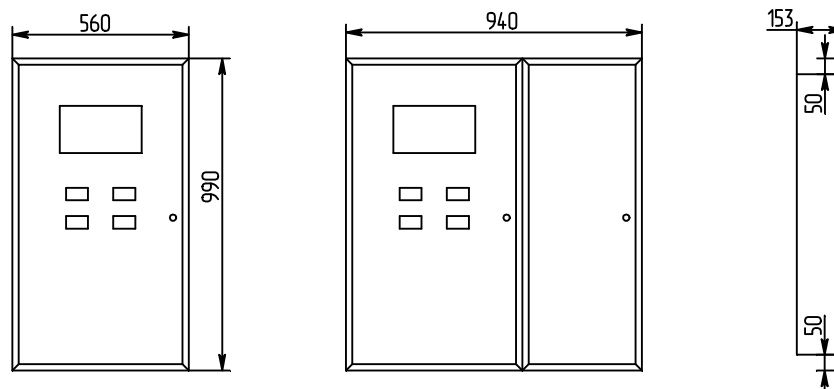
Габаритные и установочные размеры ЩЭ
